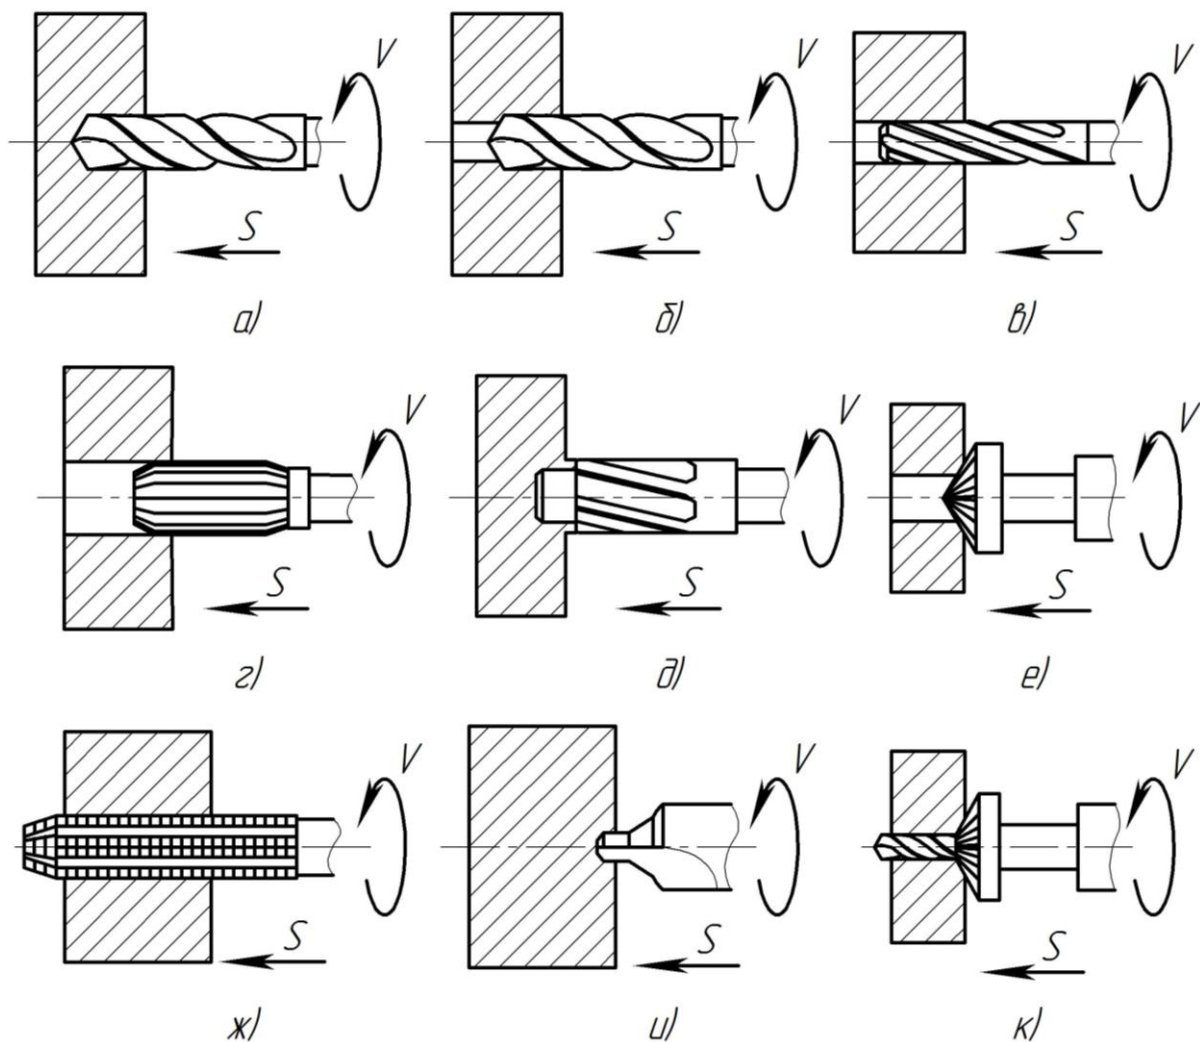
Схеми обробки отворів на свердильних верстатах
